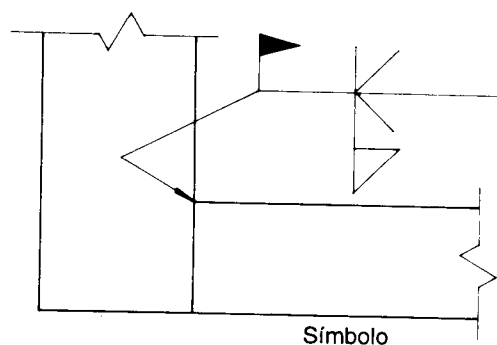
Exemplo de símbolos de soldagem de penetração total
